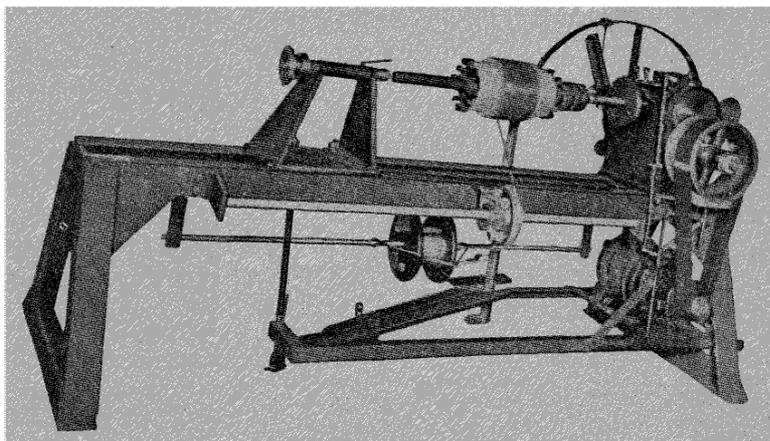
Bâti de machine spéciale entièrement soudé.
